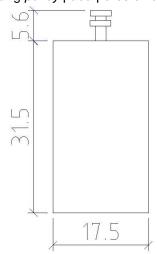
Pemasangan Bilah Pisau dengan Besi Plat Las bagian tengah bilah pisau dengan besi poros
